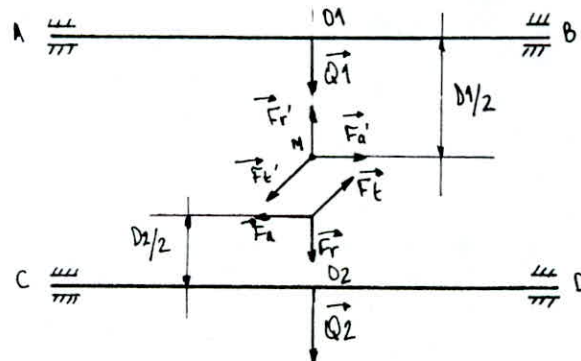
Forces appliquées : a) sur le pignon b) sur la roue
